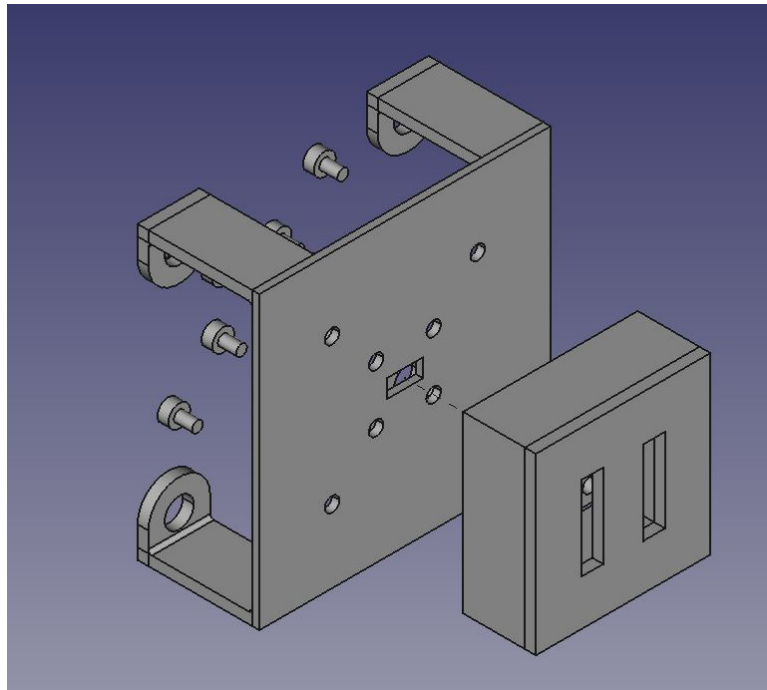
Vista explosionada del acople del sensor AS5600s, creado con FreeCAD.
